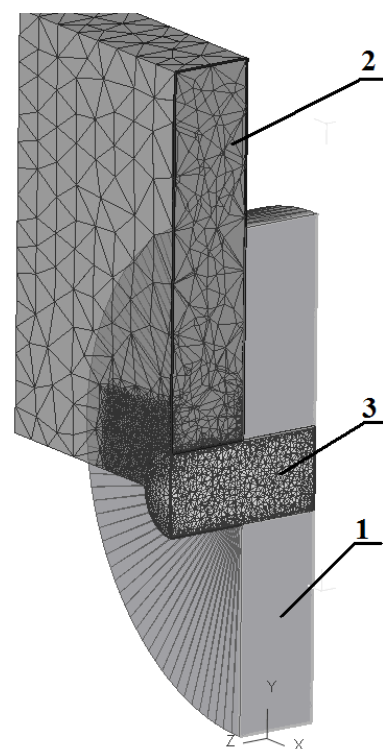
Розрахункова схема системи нерухомий ніж – дрiт – рухомий ніж:
